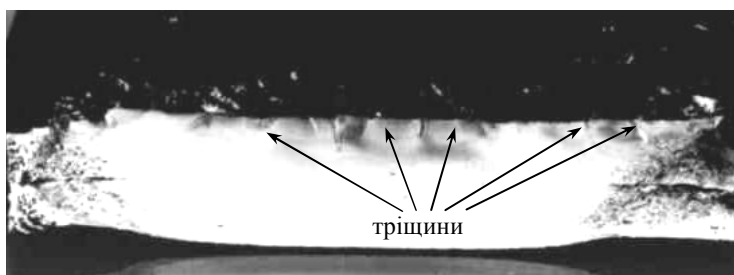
Поверхня руйнування зразка з привареною накладкою, що демонструє багатоосередковий характер зародження поверхневих тріщин
